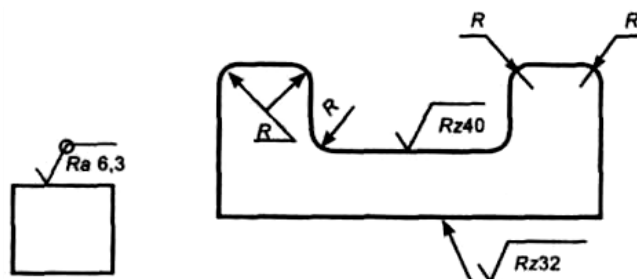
Вспомогательный знак к обозначению шероховатости
